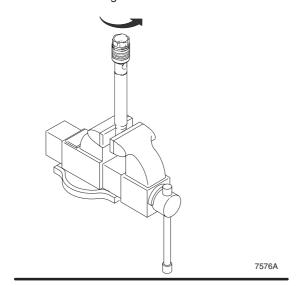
Enlever les joints et les bagues de la tige de piston.
